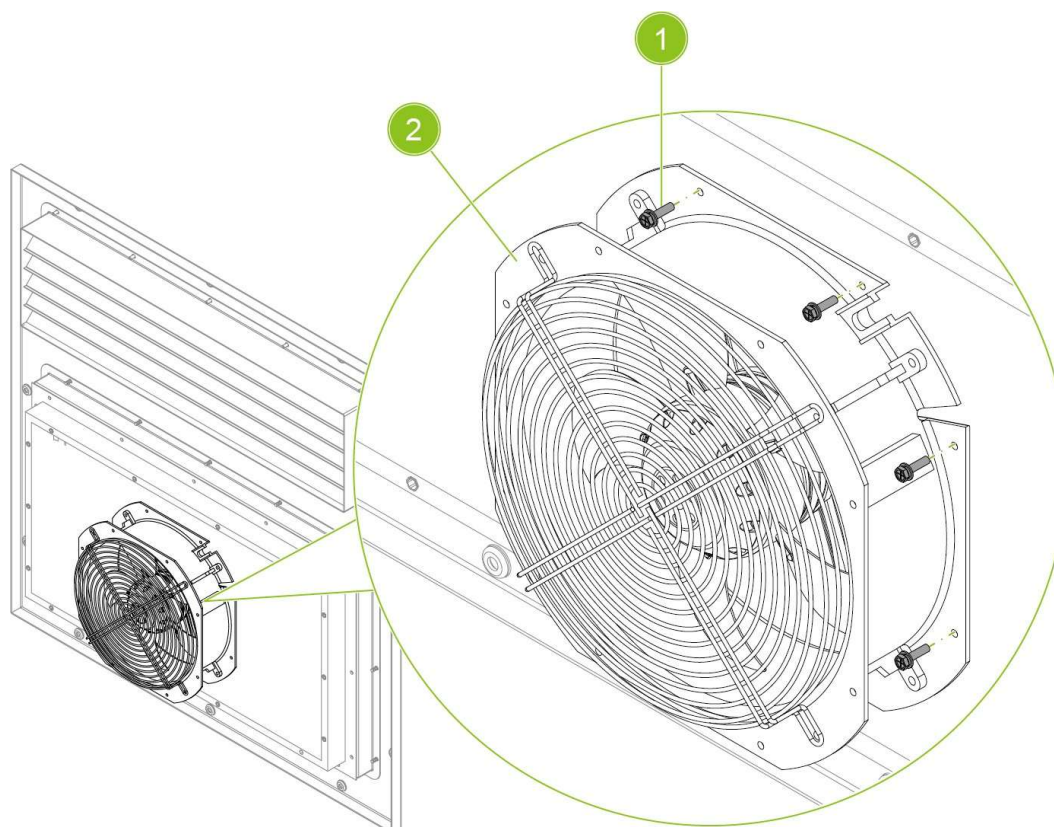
Orifícios de fixação da placa de montagem do ventilador de resfriamento
